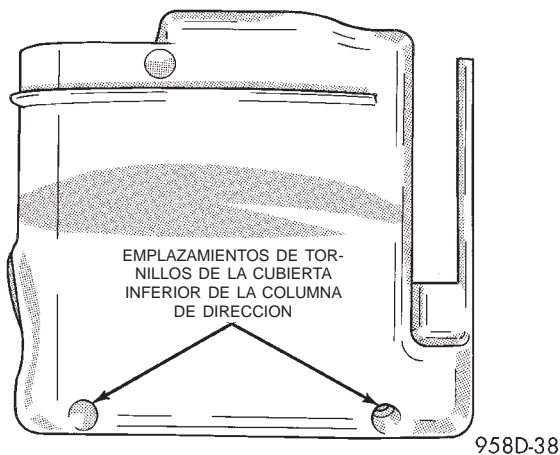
Emplazamientos de los tornillos de la cubierta inferior de la columna de dirección
